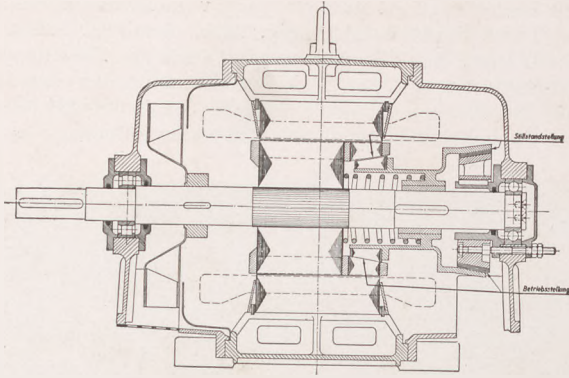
Schnitt durch die Motortype LADB mit Eigenbremsung.
